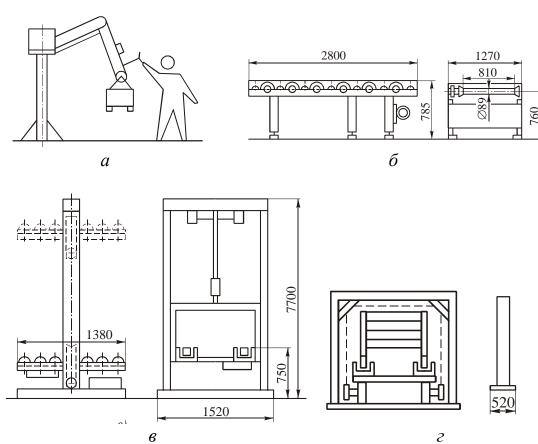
Оборудование для приема и переработки грузов на складах: a — шарнирно-балансирный многозвенный манипулятор; δ — перегрузочный роликовый приводной конвейер; ϵ — подъемник; ϵ — секция контроля габаритных размеров
